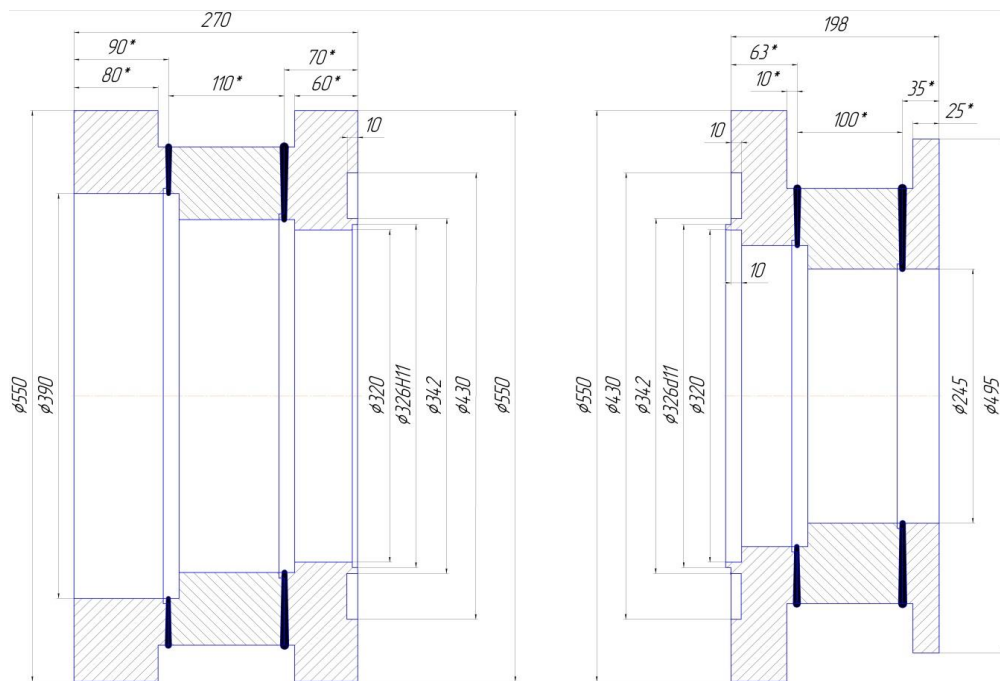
Промежуточная сварка раскатных колец заготовки шпангоута (Этап №2)
